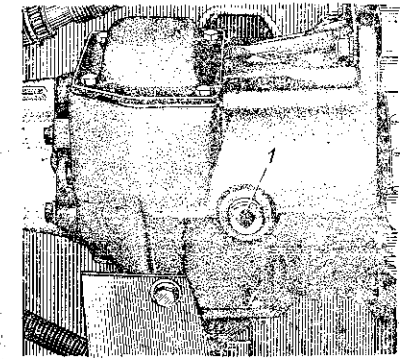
Расположение пробки сливного отверстия картера коробки передач: 1 — пробка
